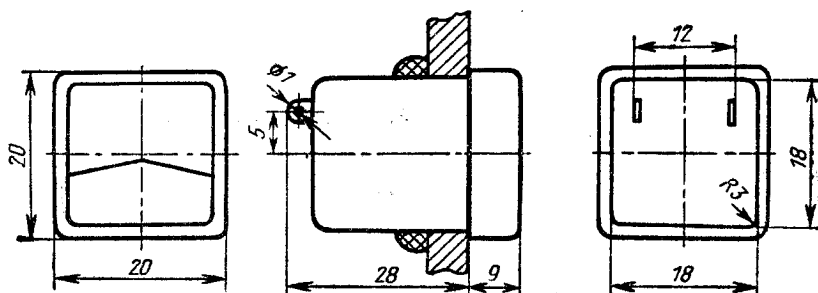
Габаритный чертеж прибора типа М4222.
